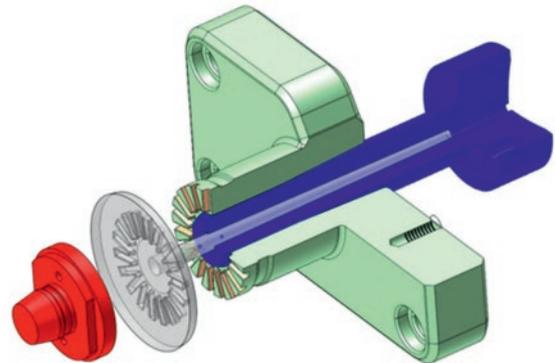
Messprinzip Torsionsmeter: Formwerkzeug (rot) tordiert gegen Bauteil (grau).
